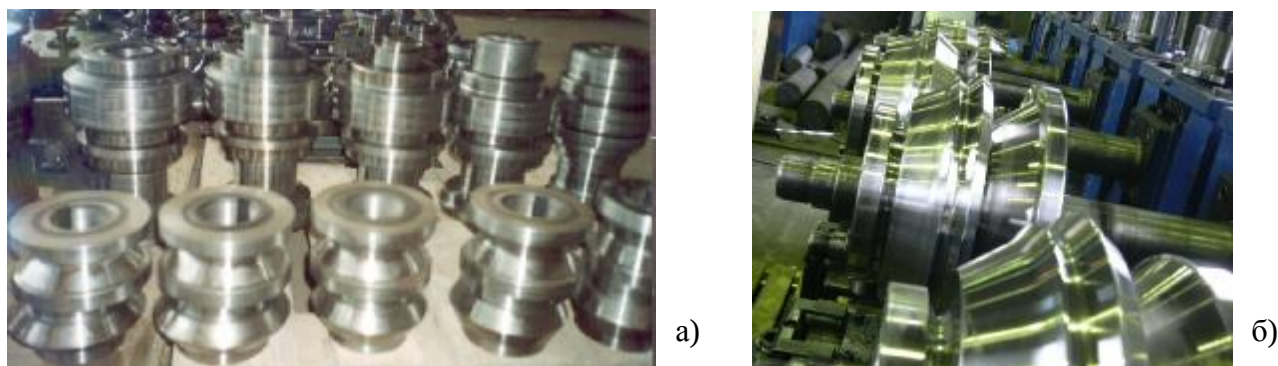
Роликовая оснастка для интенсивного деформирования: а – отдельно стоящая; б – смонтированная на рабочих валах профилировочного станка
